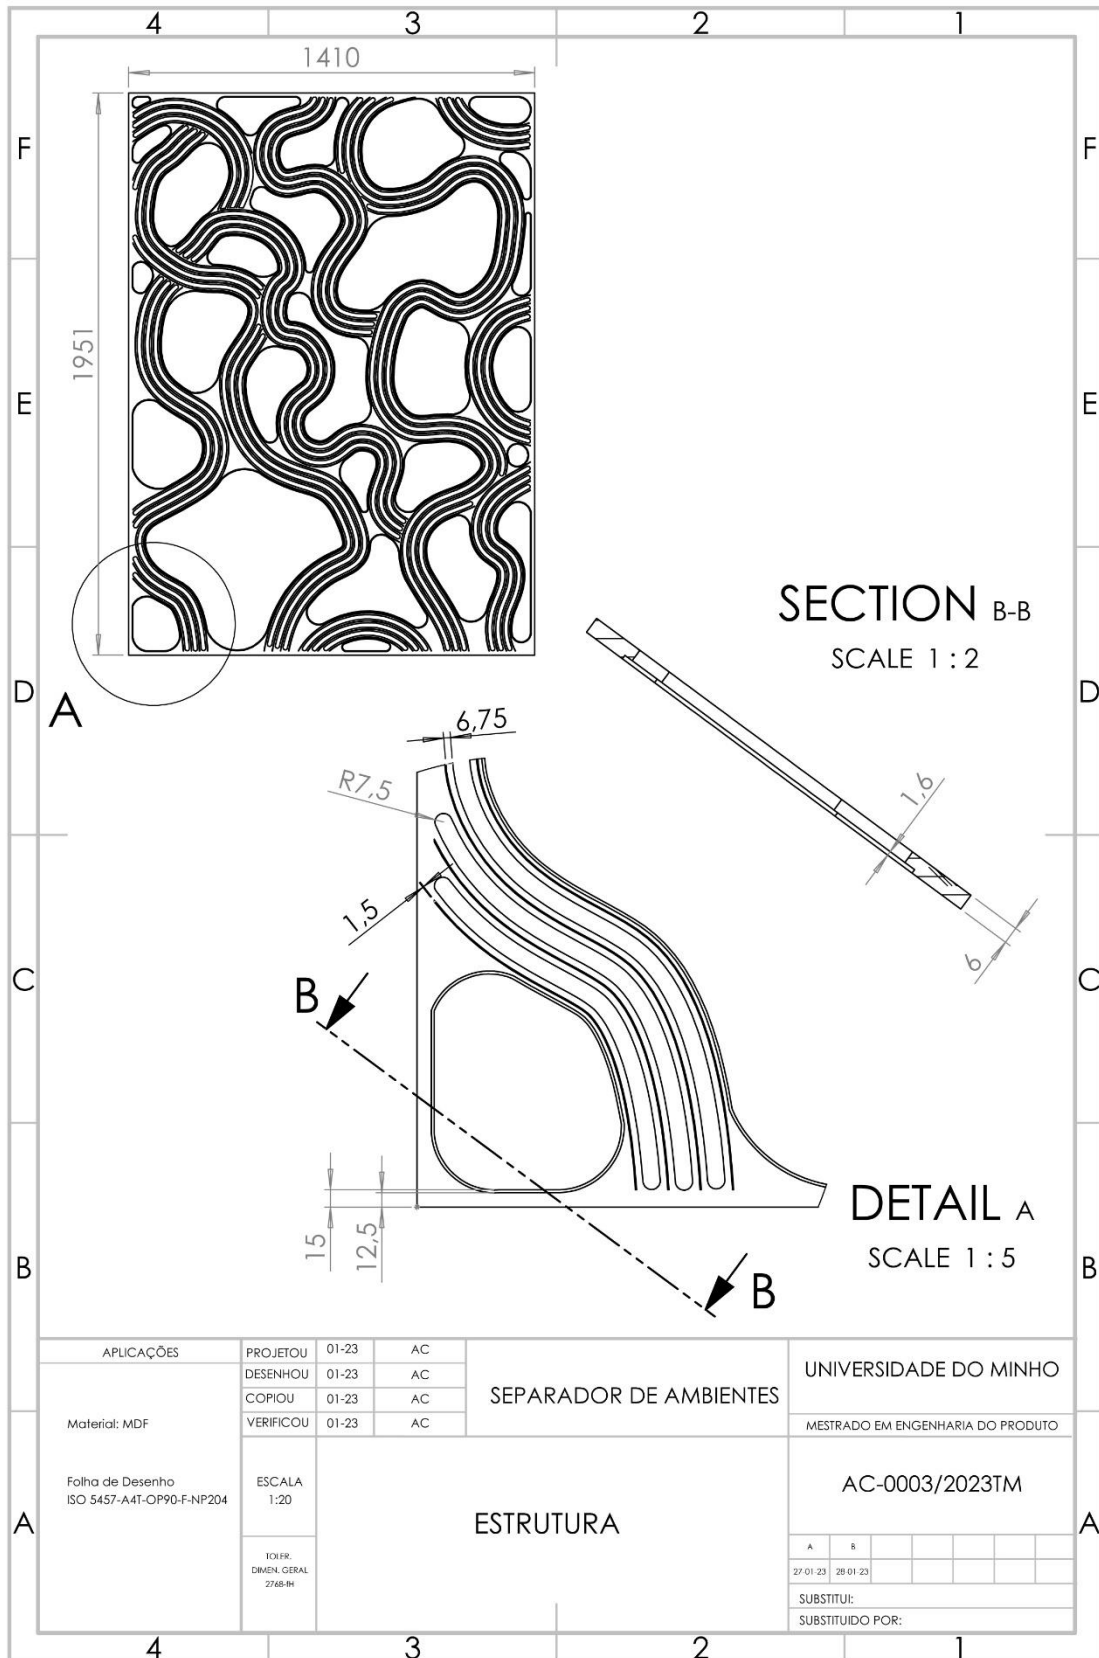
Desenho Técnico: Estrutura (parte 2)
